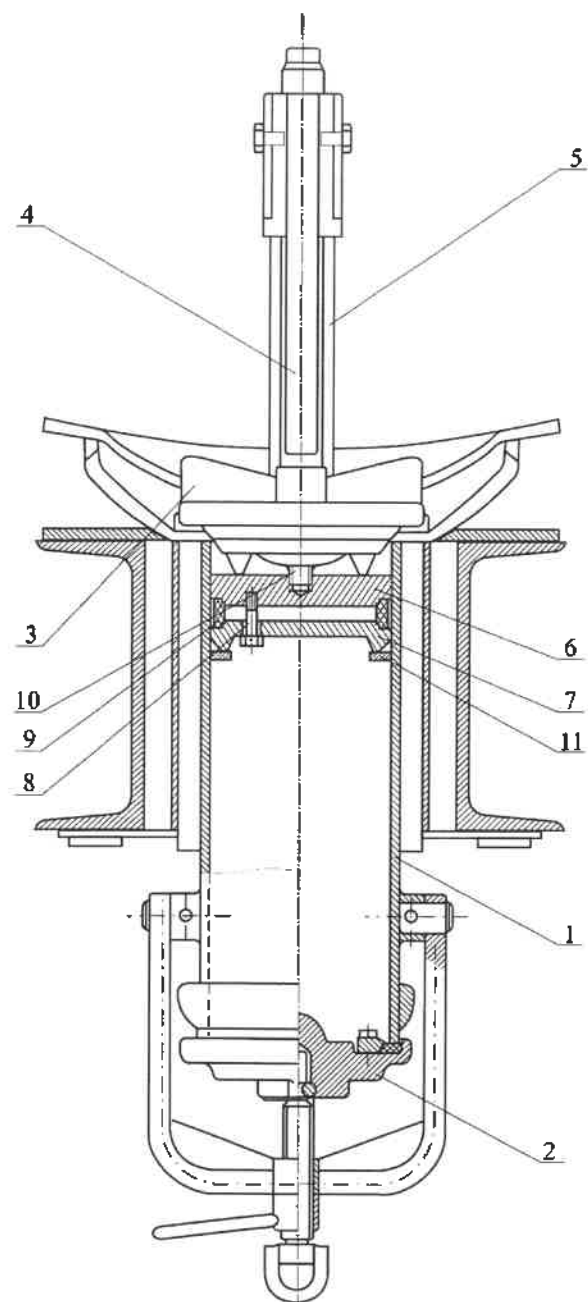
Конструкция сливного прибора с тройной защитой [8]
